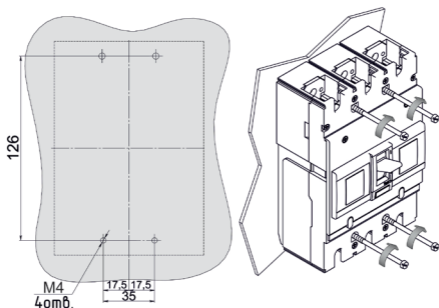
Расположение отверстий для крепления выключателя на панели
